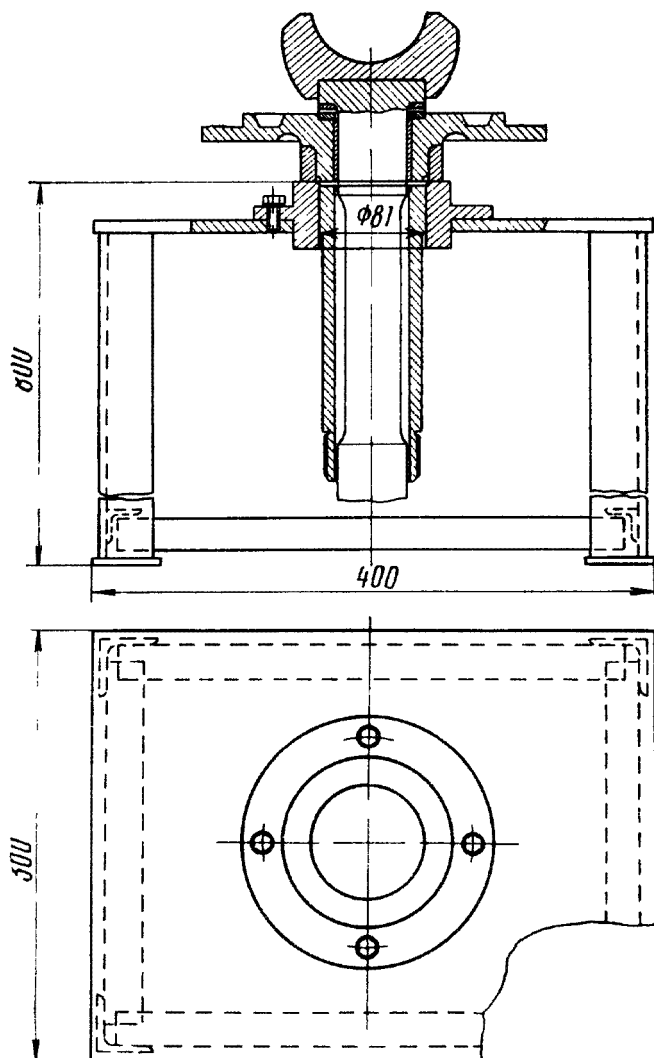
Общий вид приспособления для сборки цапфы поворотного кулака
